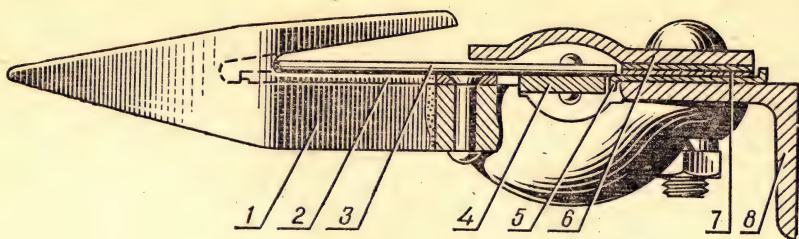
Режущий аппарат комбайнов СК-5, СК-6 и СКД-5:
